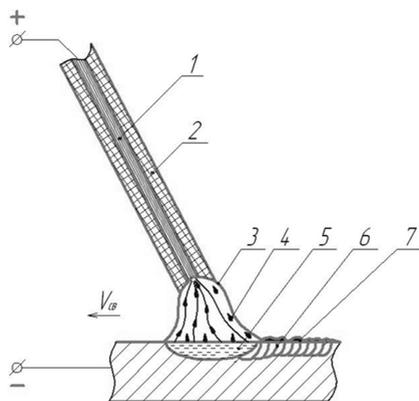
Схема электродуговой сварки покрытым металлическим электродом: 1 — электродный стержень; 2 — электродное покрытие; 3 — сварочная дуга; 4 — капли металла стержня; 5 — ванна расплавленного металла; 6 — металл сварного шва; 7 — шлак
